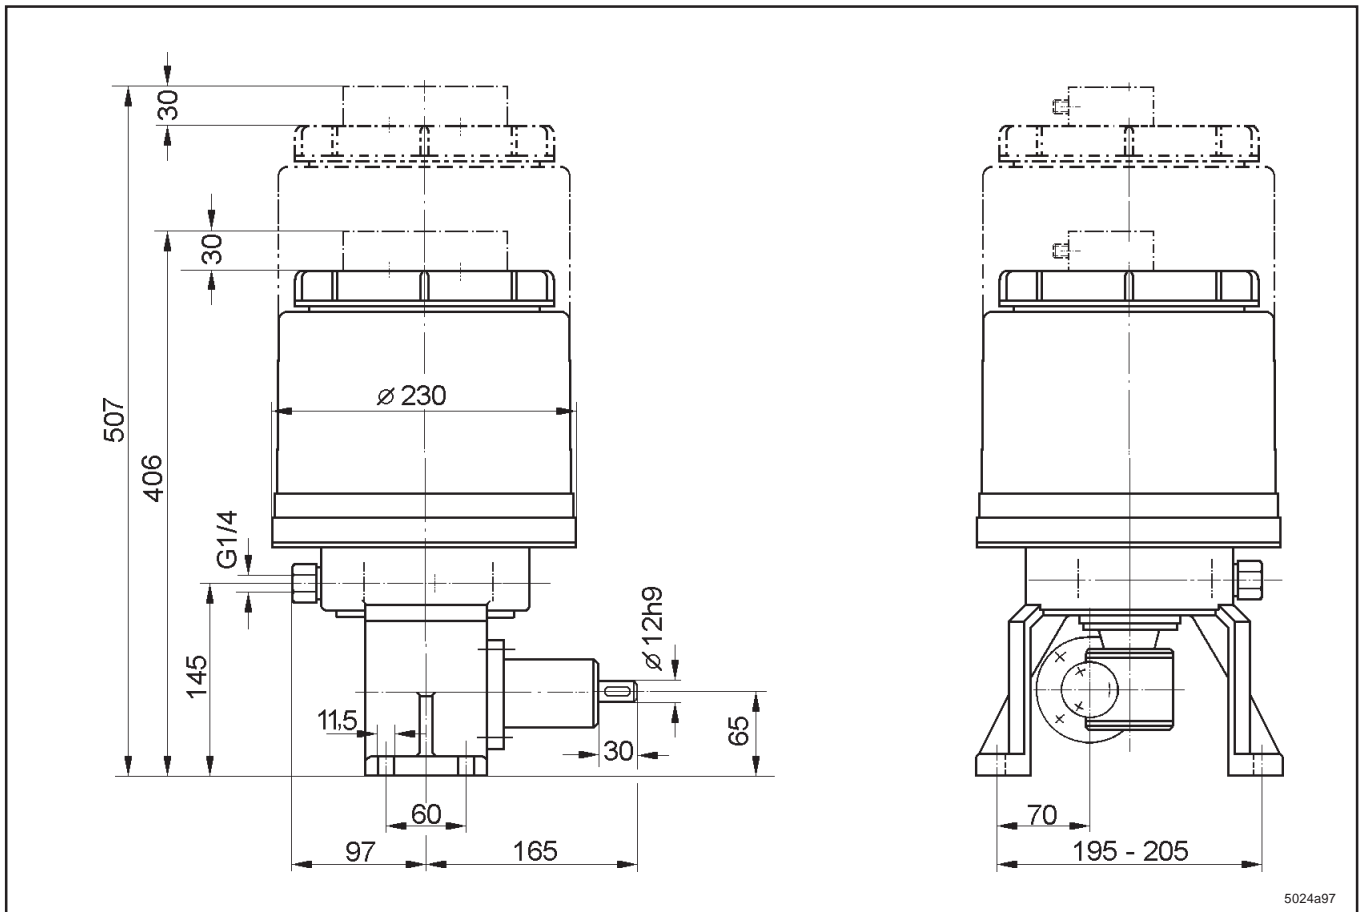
Maßzeichnung für Pumpe P 205, 1-stufiges Getriebe, 4/8l Kunststoffbehälter, freies Wellenende
